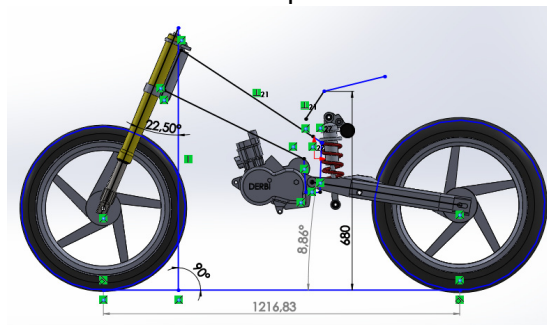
Posicionamiento de componentes sobre croquis de geometrías.
